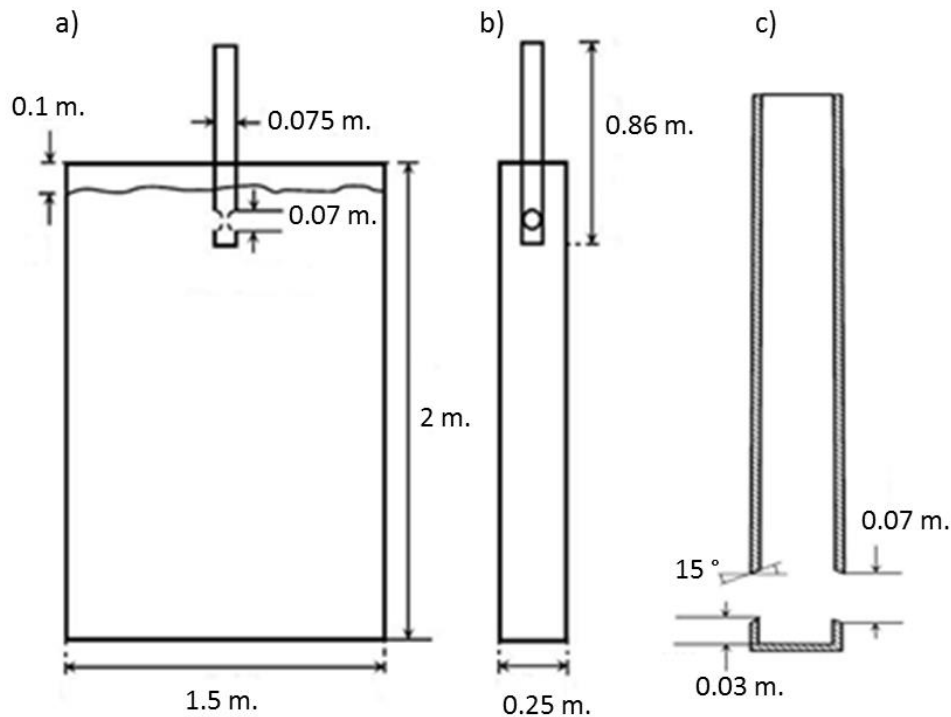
Planos del Molde y Buza. a) Vista frontal del molde, b) Vista lateral del molde, c) Vista frontal de la buza.
